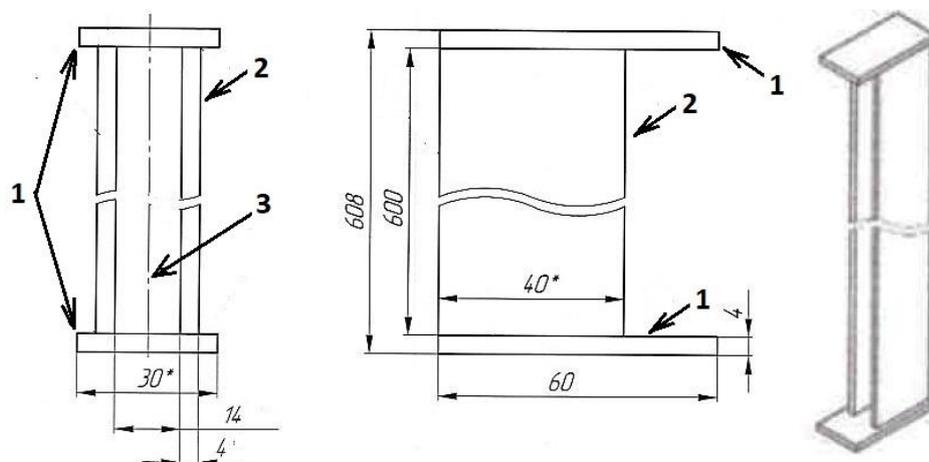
Конструкция и размеры кронштейнов ККП-60 с опорными пластинами одинаковой длины:
